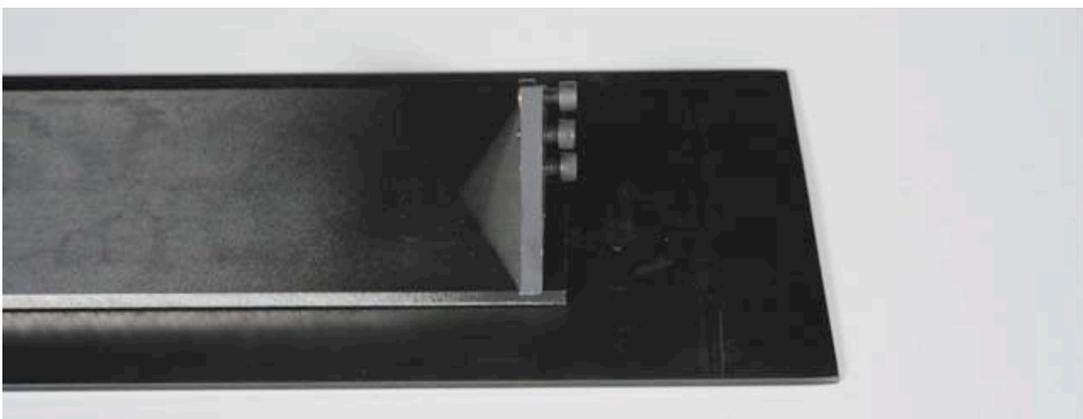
Seitenansicht des dreieckigen Befestigungsteils mit Inbusschrauben.
